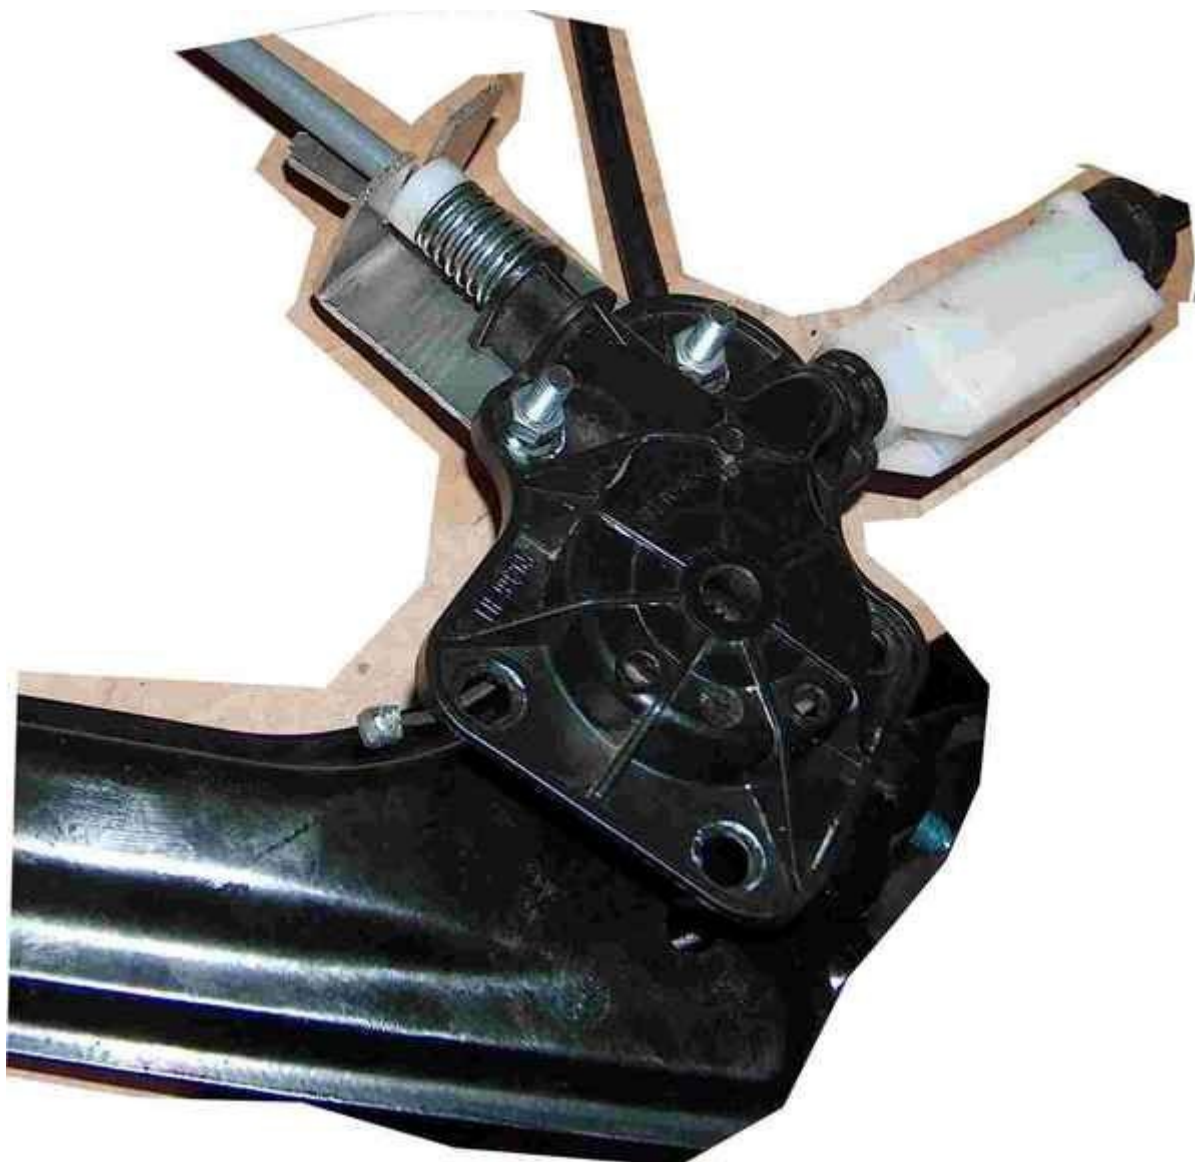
Câbles en place sur le tambour (& équerre bride ressort)
